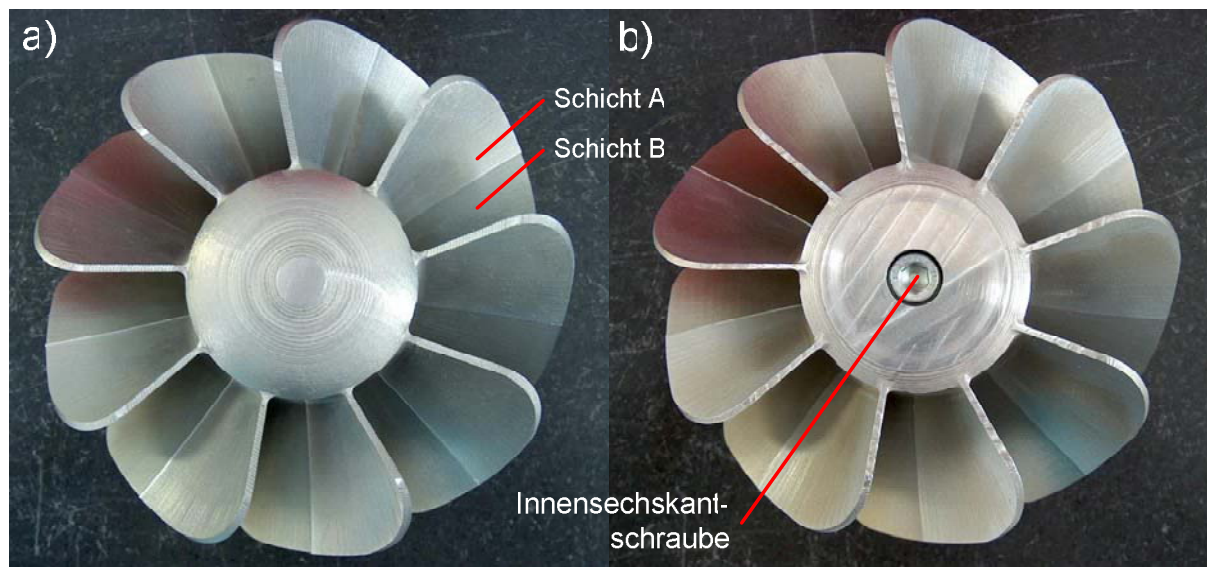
gefügter Probekörper: a) Draufsicht b) Unteransicht
